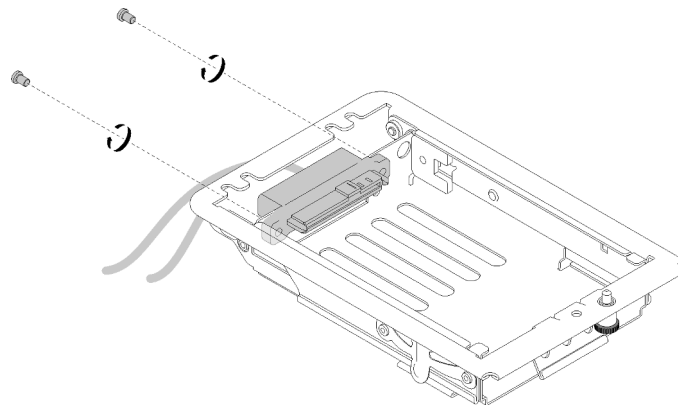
Entfernen der Schrauben – 1x2,5-Zoll-Laufwerkmodell
